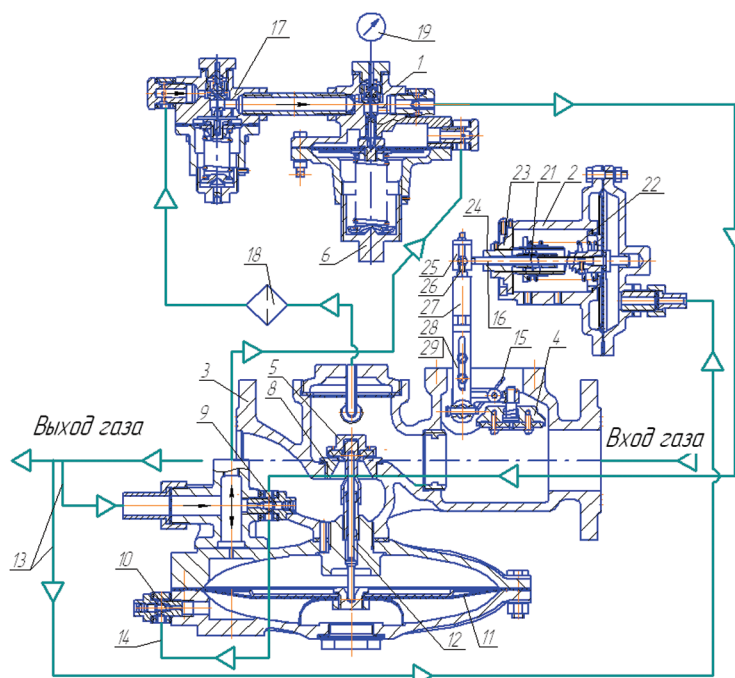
Общий вид и габаритные размеры регуляторов РДГ-Н
